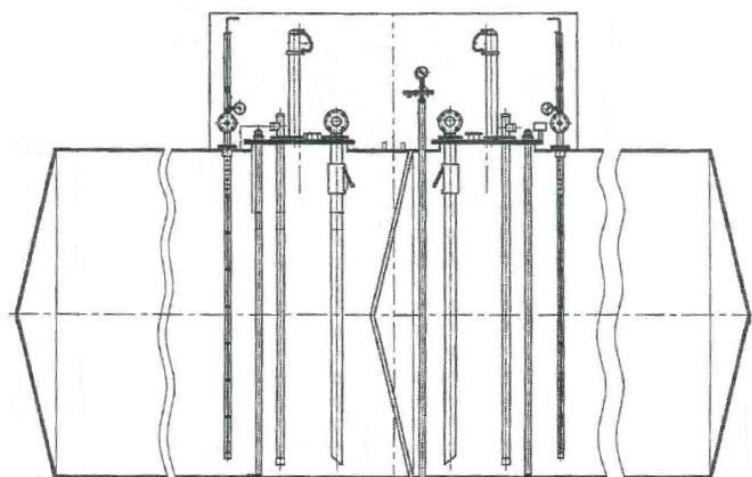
Общий вид эскиза резервуара РГС-50 зав.№ 2(12-1, 12-2)
